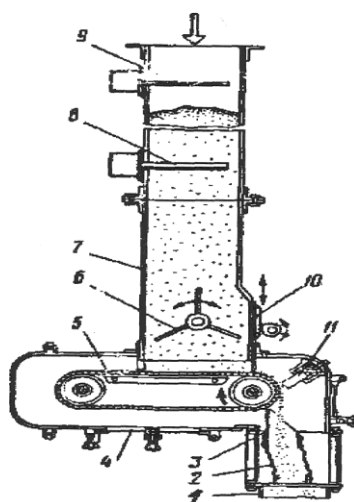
Стрічковий дозатор муки ШД-1М безперервної дії: 1 – патрубок; 2 – продукт; 3 – течія; 4 – вікно; 5 – конвеєр; 6 – зворошувач; 7 – шахта; 8, 9 –сигналізатор; 10 – заслінка; 11 – магніт.
